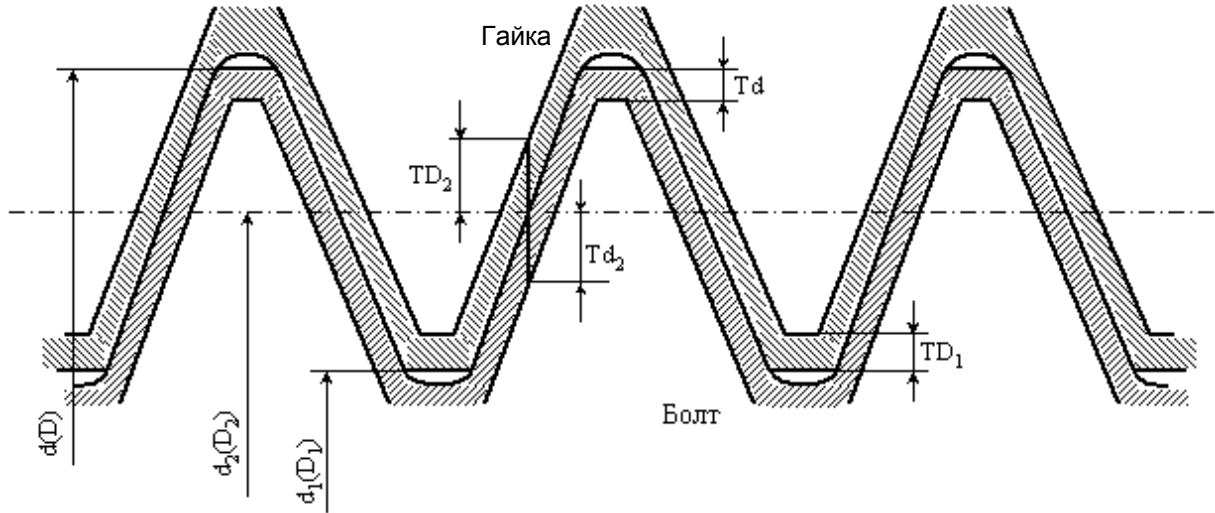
Схема расположения полей допусков резьбы
